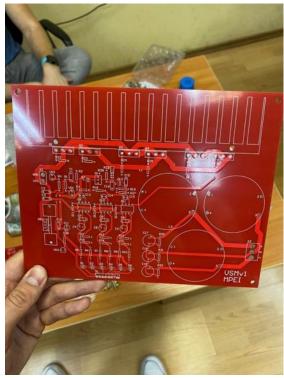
Изготовленная печатная платы для первой версии конвертора
